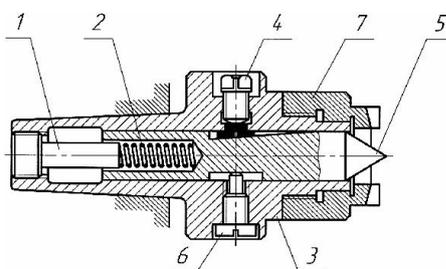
Поводковая оправка: 1–упорный винт; 2–пружина; 3– корпус; 4– стопорный винт; 5–подпружиненный (плавающий) центр; 6– винт; 7– зубья/штырьки
